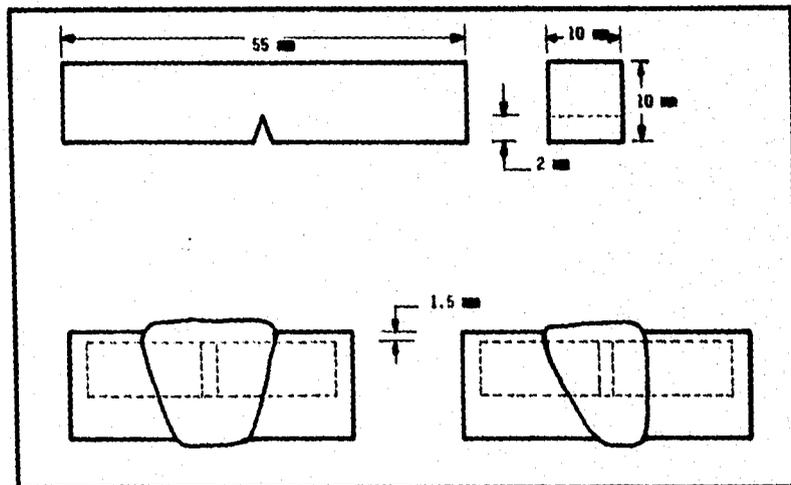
DIMENSIONES DE PROBETAS DE IMPACTO.
